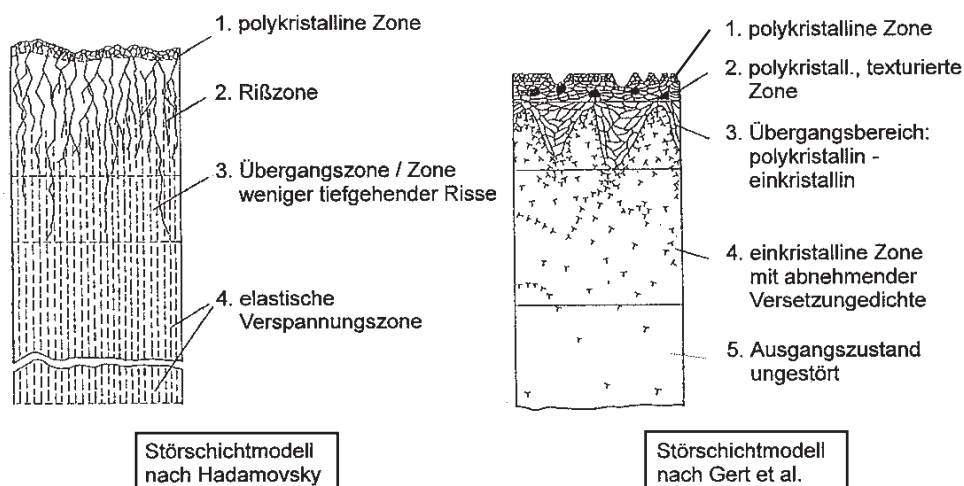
Störschichtmodelle für mechanisch bearbeitete Werkstoffe [92] [93]
